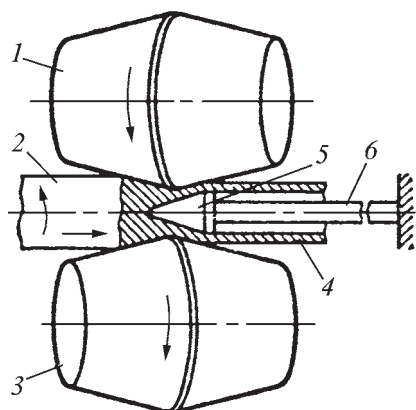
Схема косой (винтовой) прокатки труб (вид сверху):
